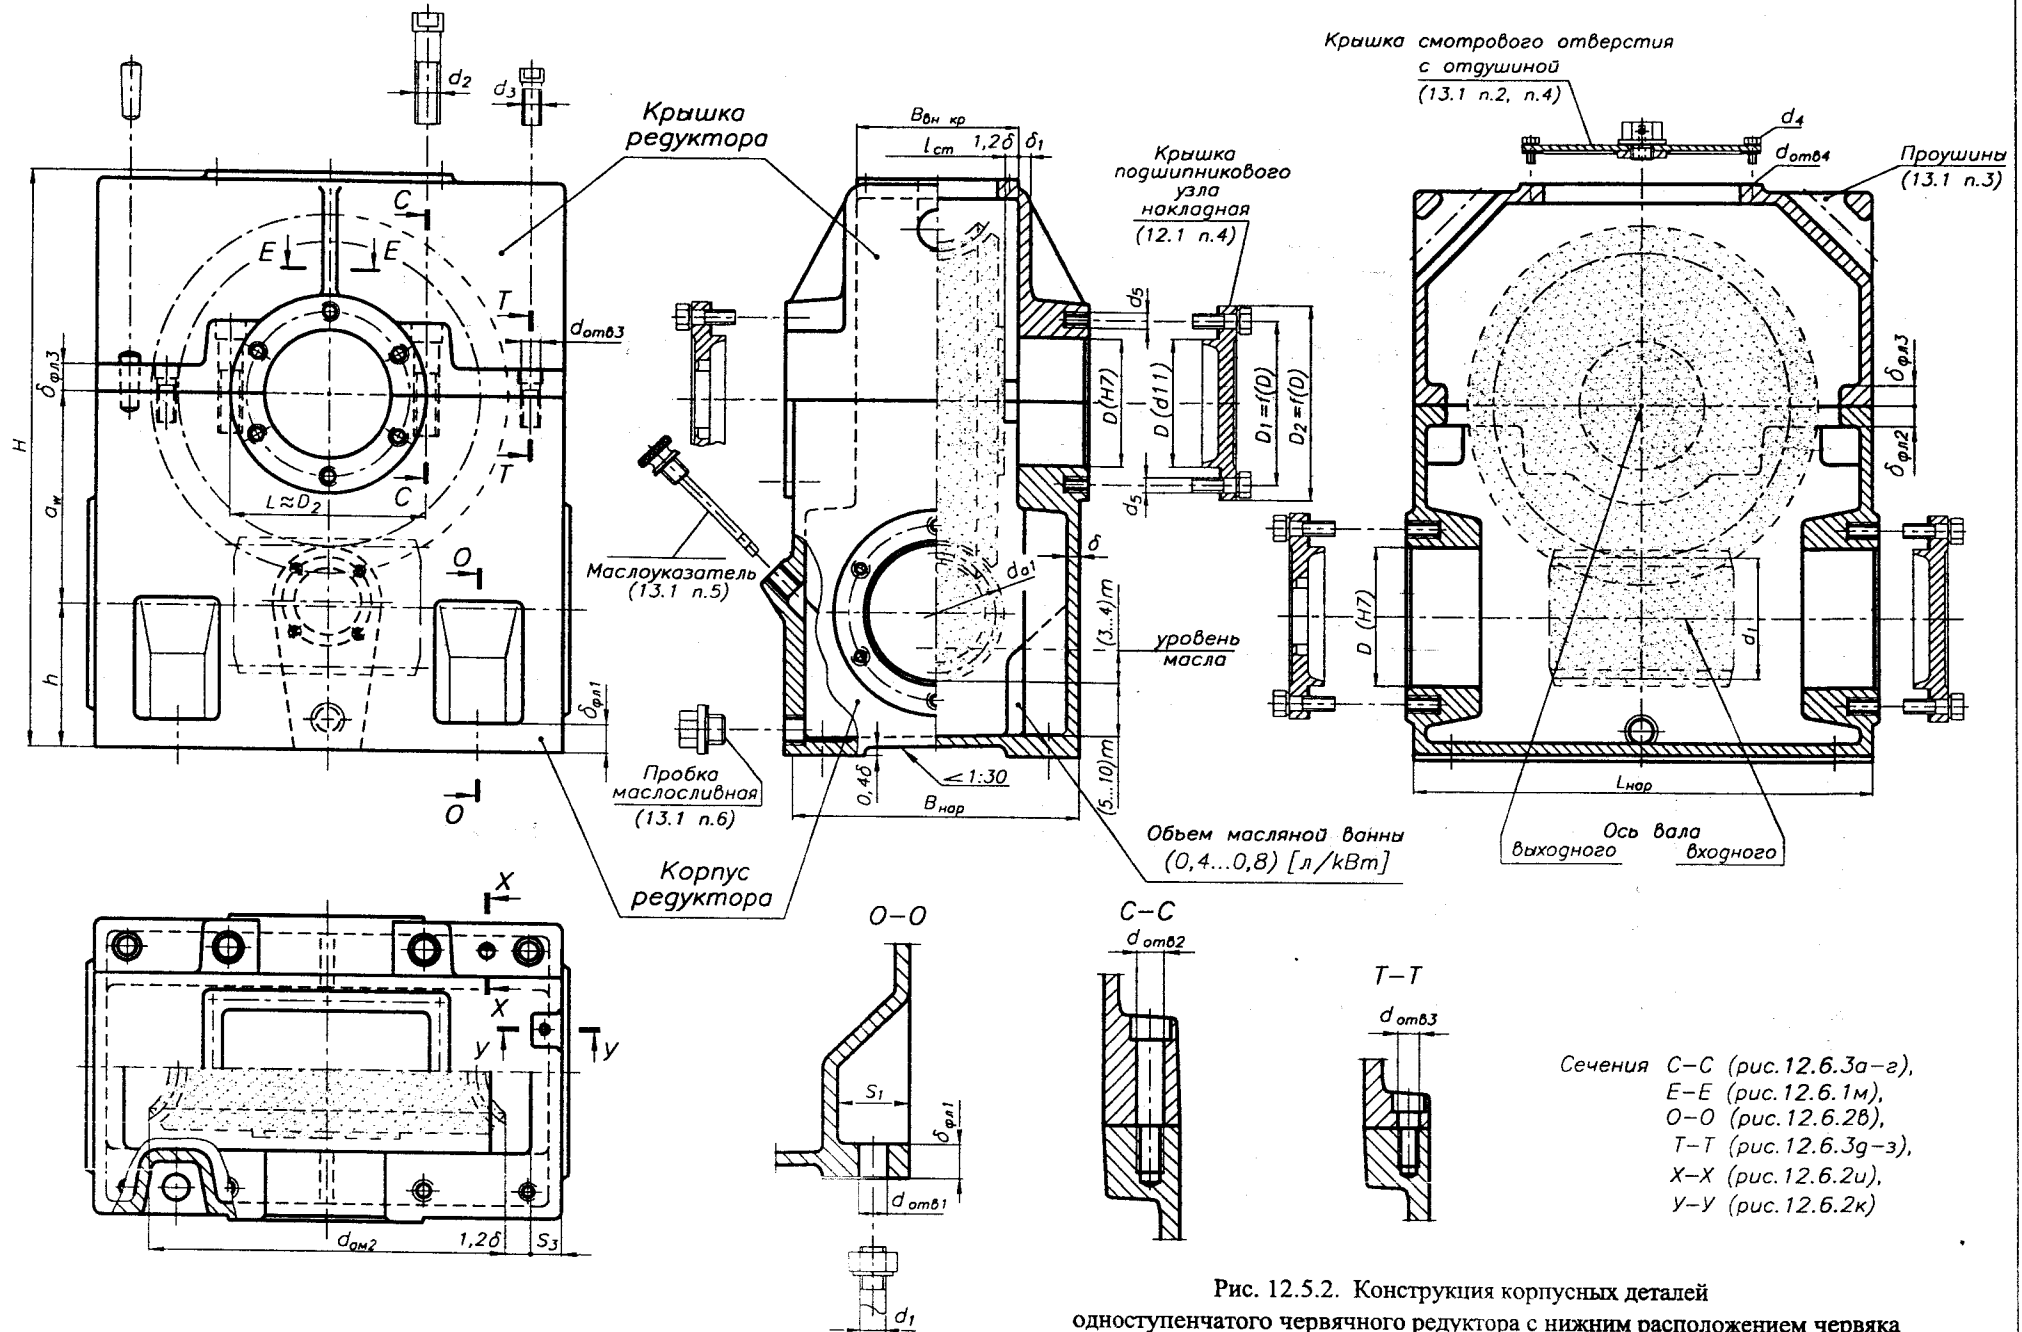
Конструкция корпусных деталей одноступенчатого червячного редуктора с нижним расположением червяка при внутреннем размещении подшипниковых бобышек
